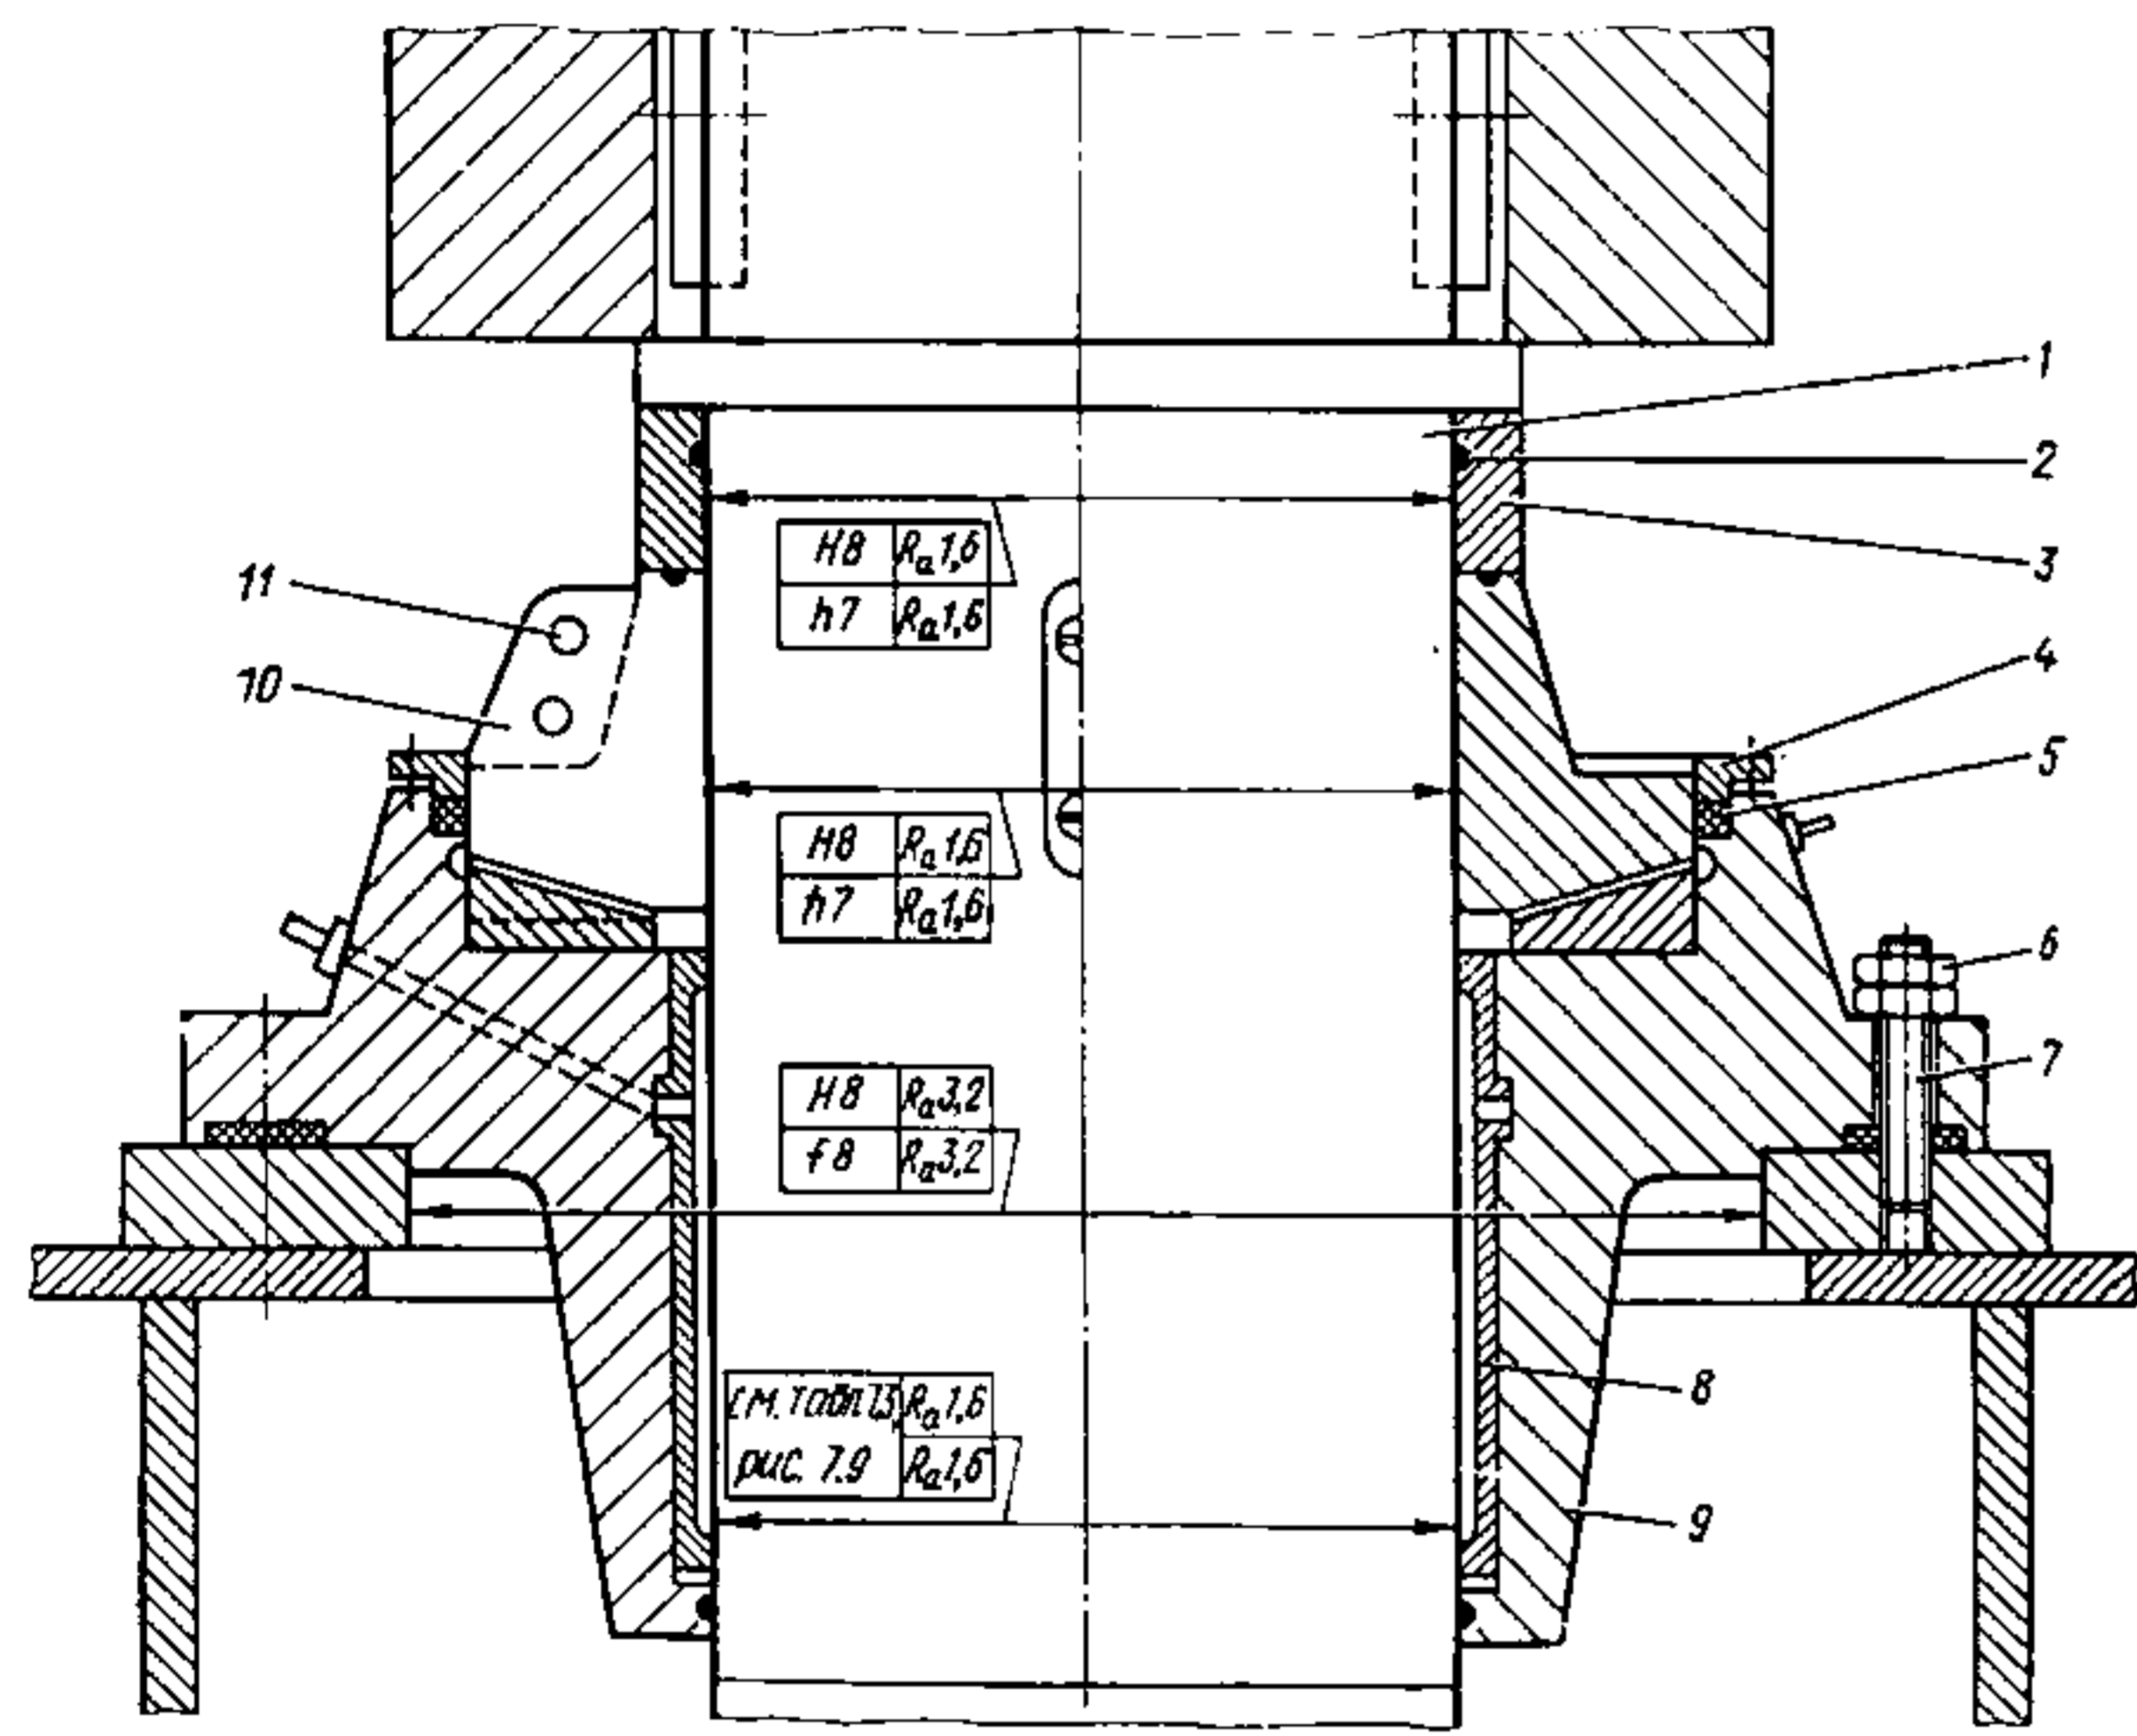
Опорно-упорный подшипник баллера:
